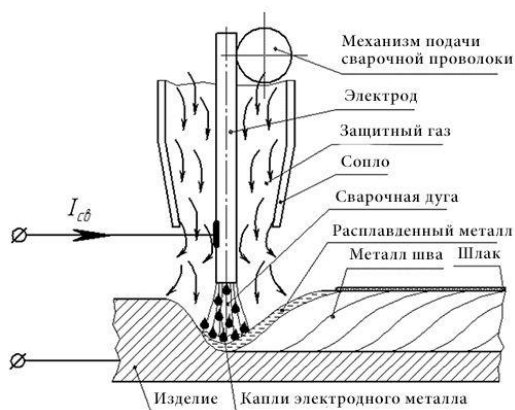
Механизированная сварка в среде защитного газа
